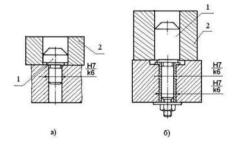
Схемы установки детали на установочных пальцах: a) на низком установочном пальце; б) на высоком установочном пальце.
